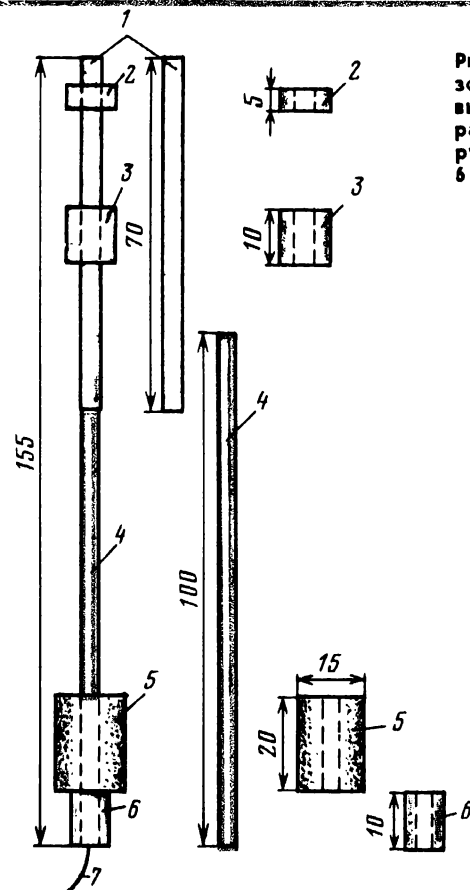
Сигнализатор в сборе: 1 — отрезок ниппельной резинки; 2, 3 — резиновые колечки для крепления сигнализатора; 4 — отрезок стержня шариковой ручки; 5 — цилиндрок из пенопласта; 6 — хлорвиниловая трубочка; 7 — леска.
